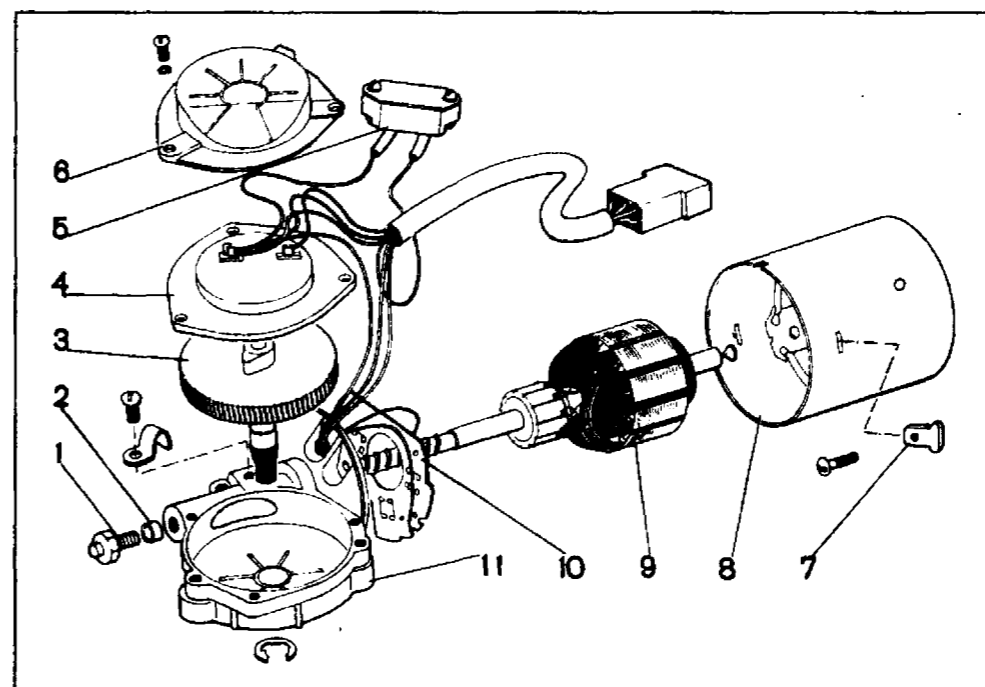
Детали моторредуктора очистителя ветрового стекла: 1 — упорный винт; 2 — подпятник; 3 — шестерня редуктора; 4 — панель; 5 — термобиметаллический предохранитель; 6 — крышка; 7 — сухарь; 8 — корпус электродвигателя; 9 — якорь; 10 — щеткодержатель; 11 — корпус редуктора
